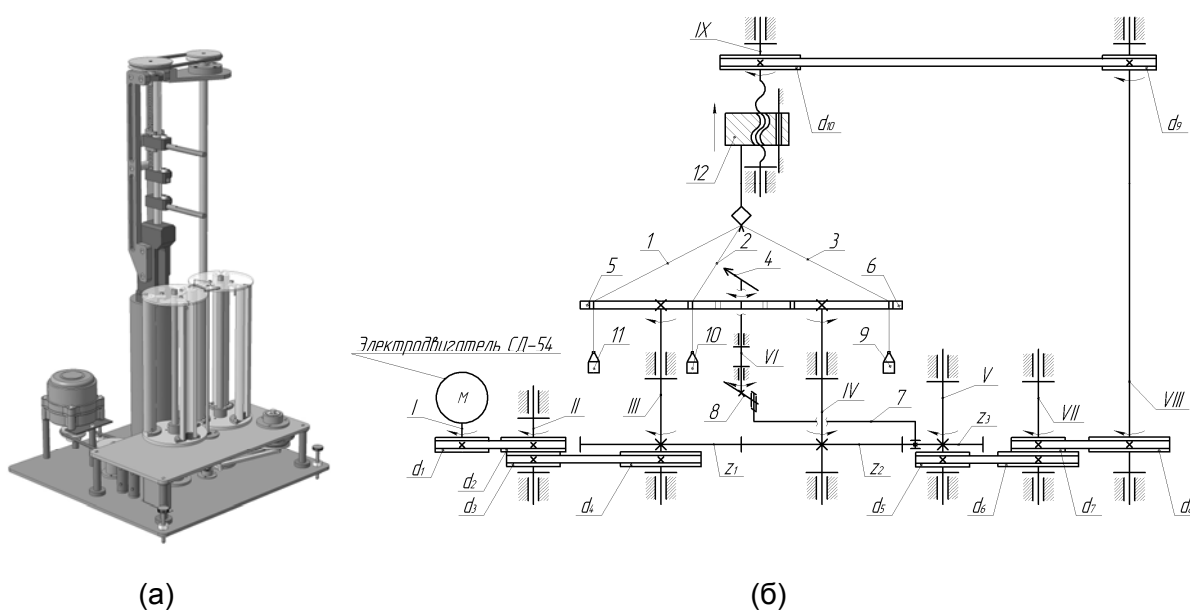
Внешний вид устройства для изготовления САН (а); кинематическая схема (б):
